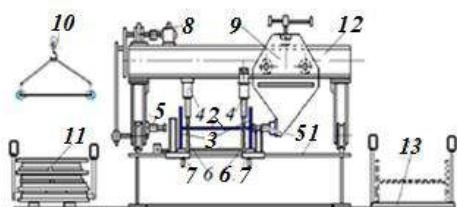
Стенд им. инженера Костюхина для сборки балочных конструкций
